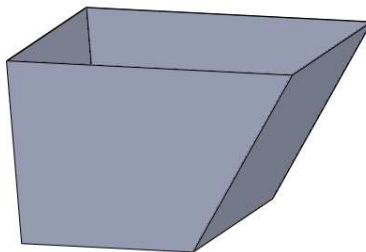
16 Recipiente de almacenamiento fijo a la máquina
